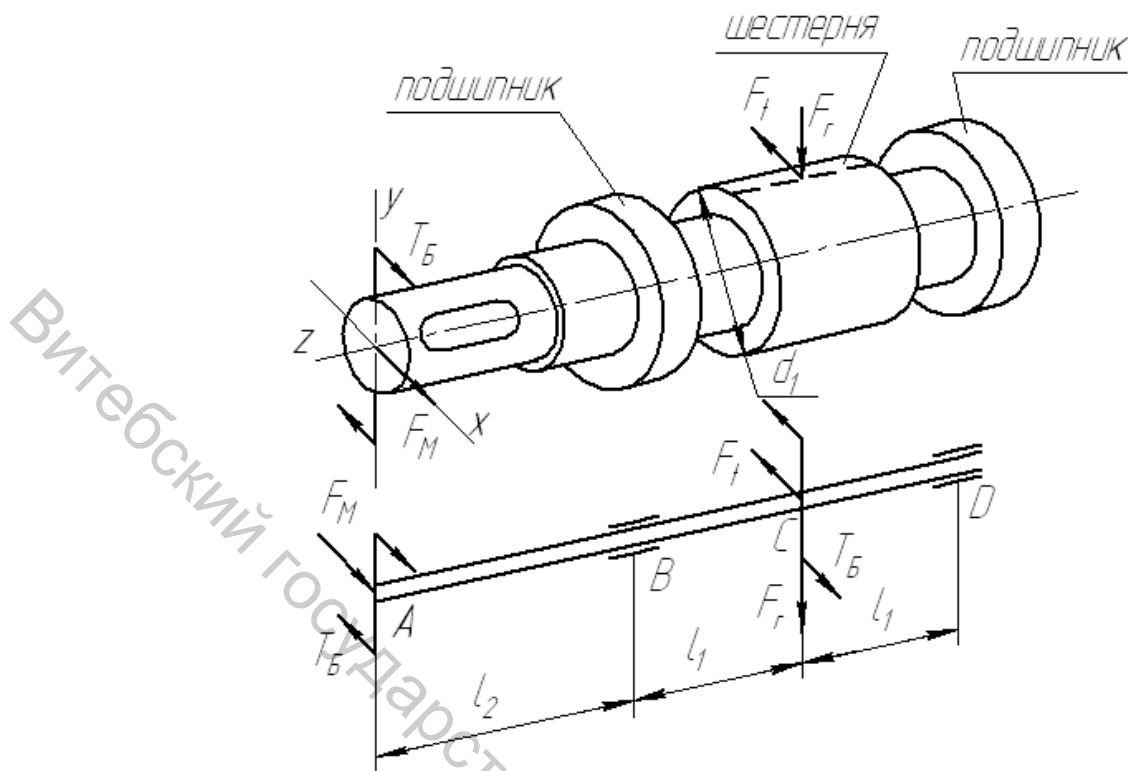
Быстроходный вал редуктора и его расчетная схема
